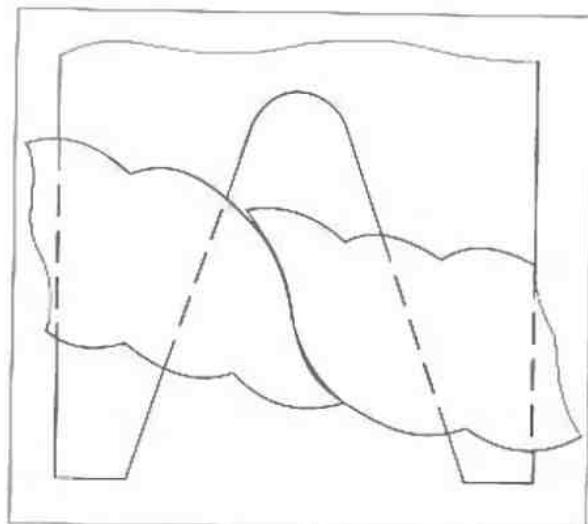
Доска с вырезом (приспособление для подгонки стыков деталей)
